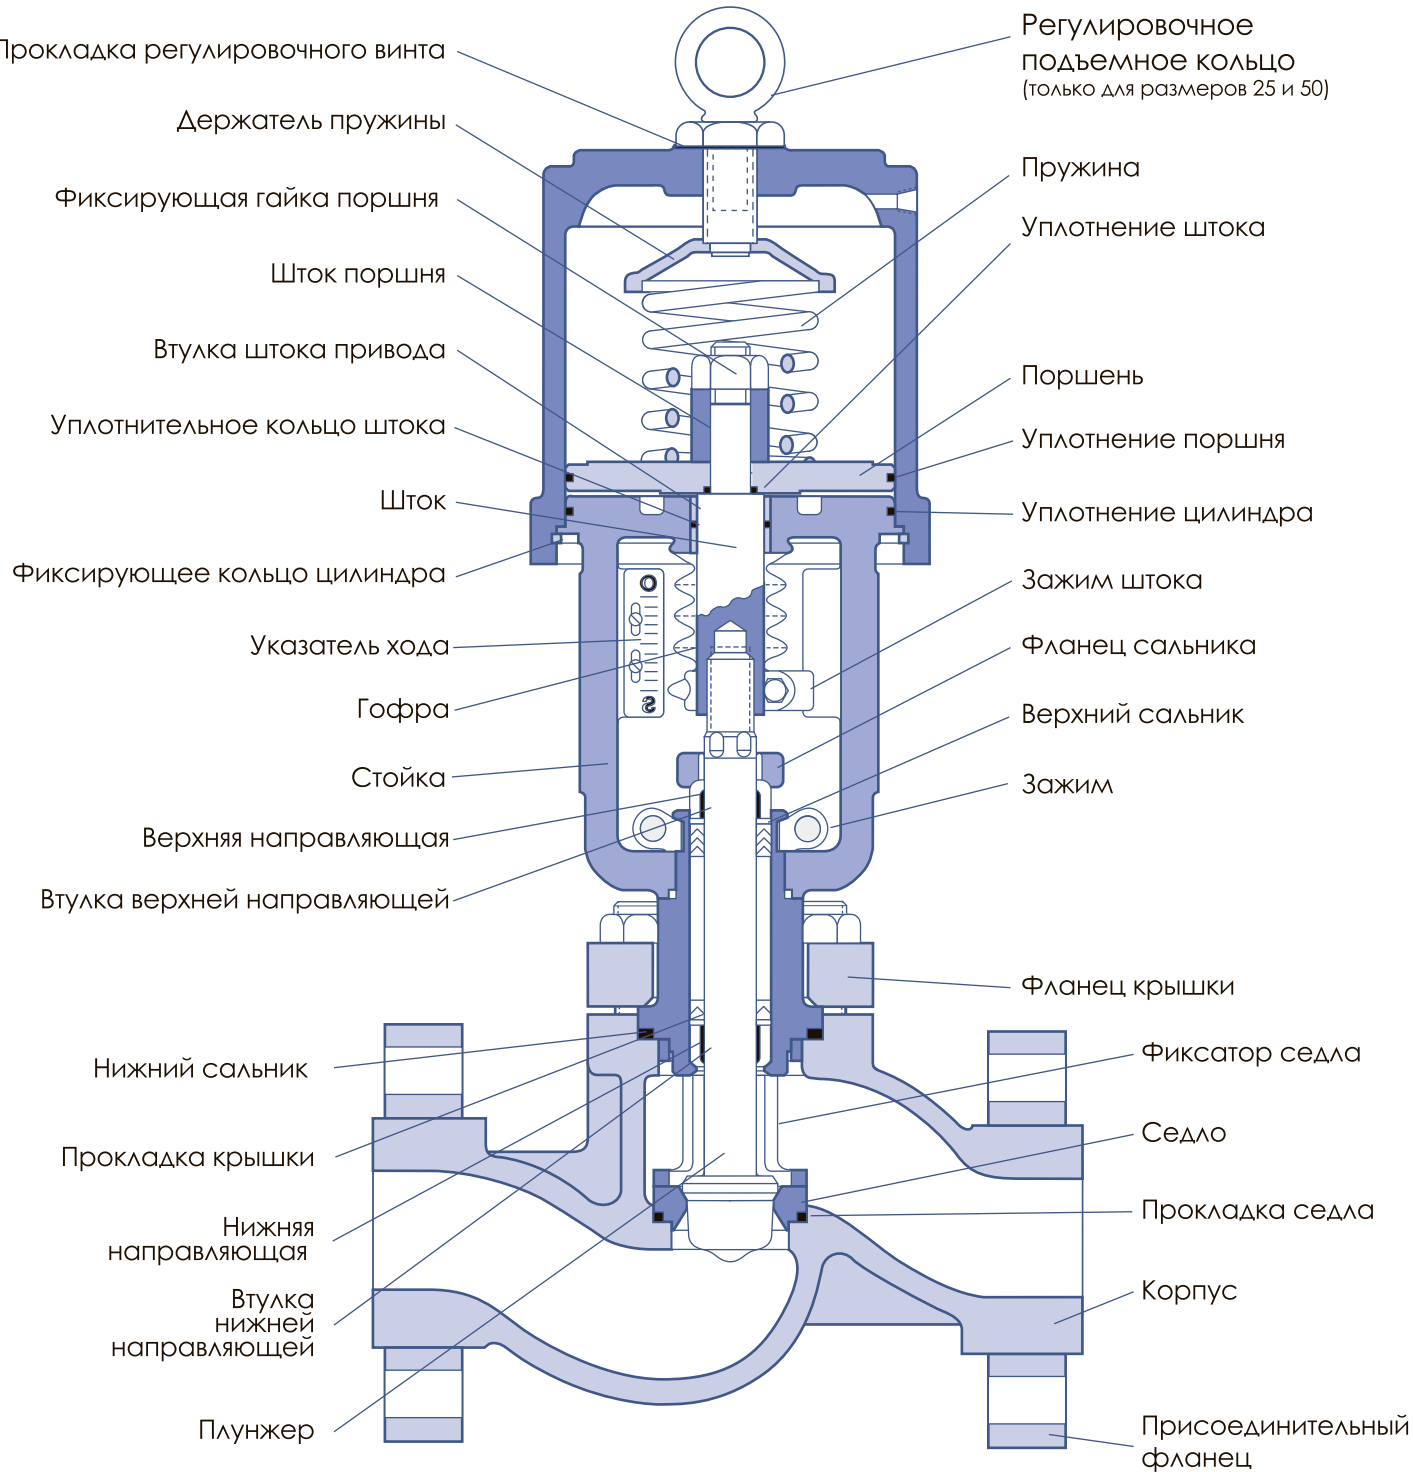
GF корпус в сборе, Класс 150, 300, и 600, PN 16, 40, 100
